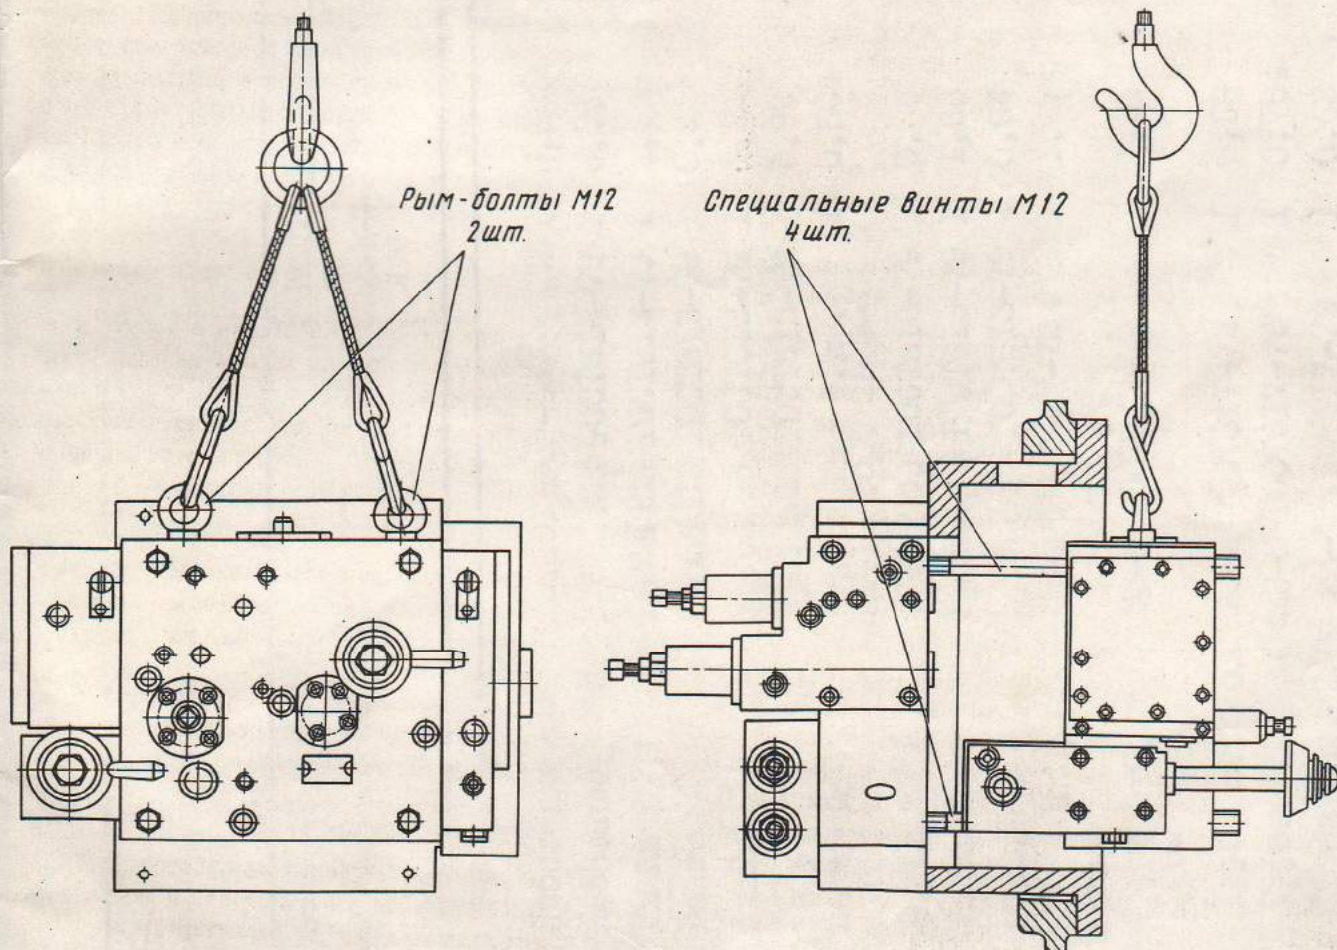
Схема монтажа и демонтажа блока управления гидропанели ГЗІ-26-01
